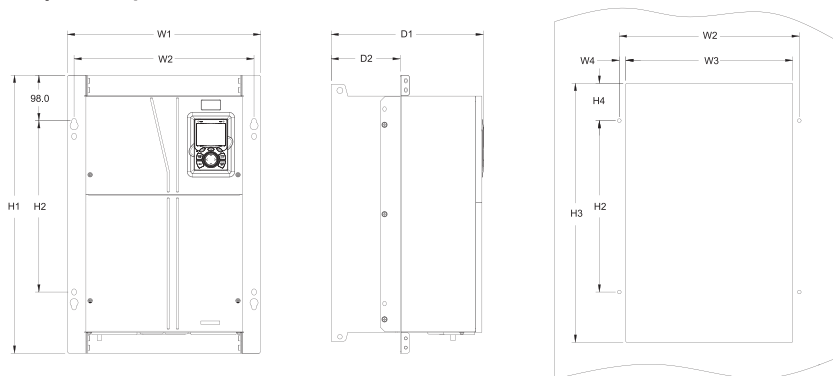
Схема ПЧ фланцевого монтажа 660 В, от 22 до 132 кВт
